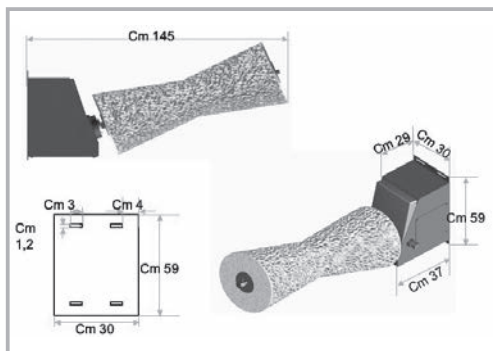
RotaBrush Classic: assieme e particolare piastra fissaggio a parete
